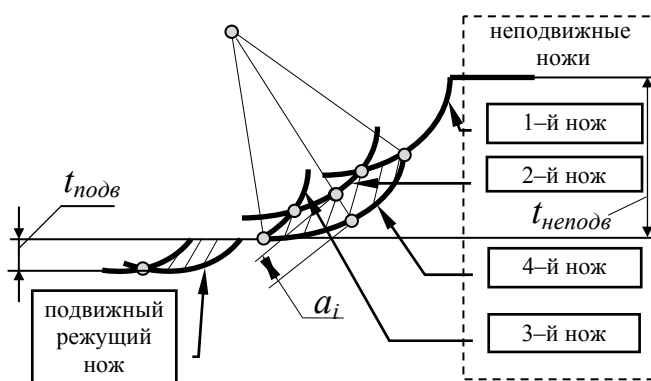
Формообразование поверхности в направлении параллельном подаче заготовки при обработке торцовой фрезой с комбинированной схемой резания
